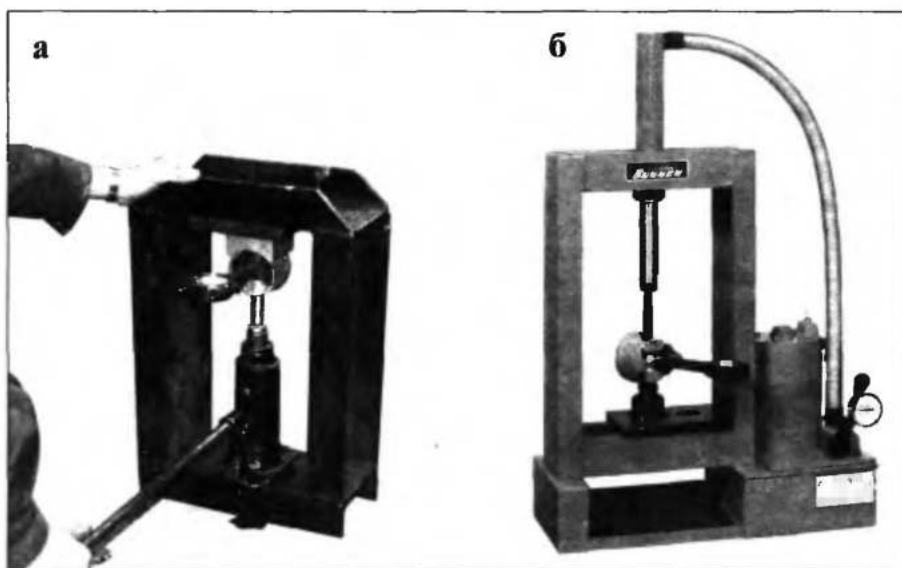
Приспособления для выпрессовки поршневых пальцев: а — рама с гидравлическим домкратом; б — специальный пресс с гидроприводом
